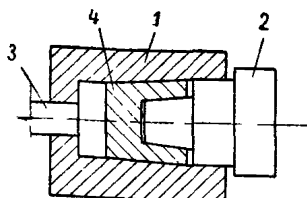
Схема конструкции штампа для изготовления электродов холодным прессованием
